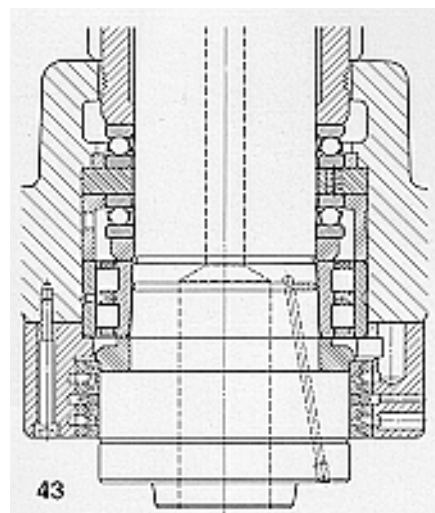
Подшипниковый узел с пружинным предварительным натягом упорных шарикоподшипников
